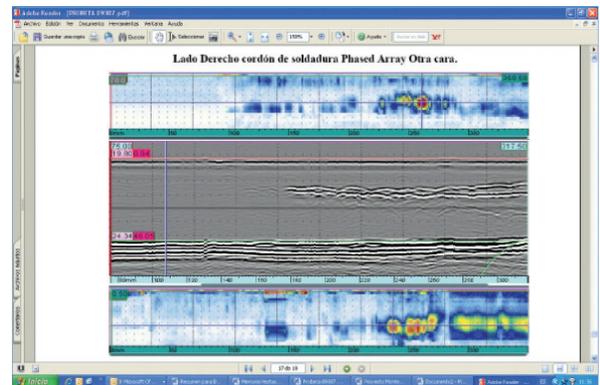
Resultado de Inspección conjunta Phased Array TOFD de unión soldada.
